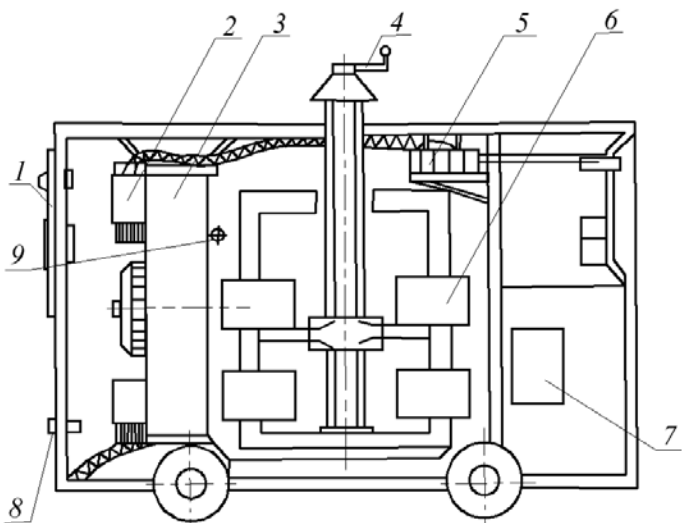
Конструктивная схема сварочного выпрямителя ВД-306УЗ:
